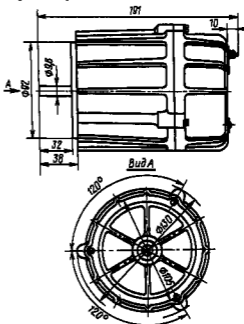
8 Габаритные и установочные размеры двигателя ДМ-3
